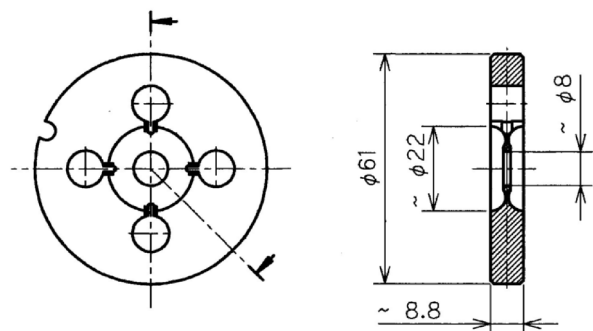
：RDDS(Rounded Damped Detuned Structure)タイプの加速管ディスク
